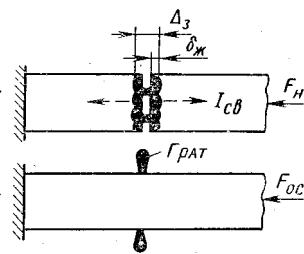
Схема образования соединения при стыковой сварке оплавлением (F_h – начальное усилие; F_{oc} – усилие осадки; Δ_3 - зазор между деталями; $\delta_{жк}$ - слой расплавленного металла).
